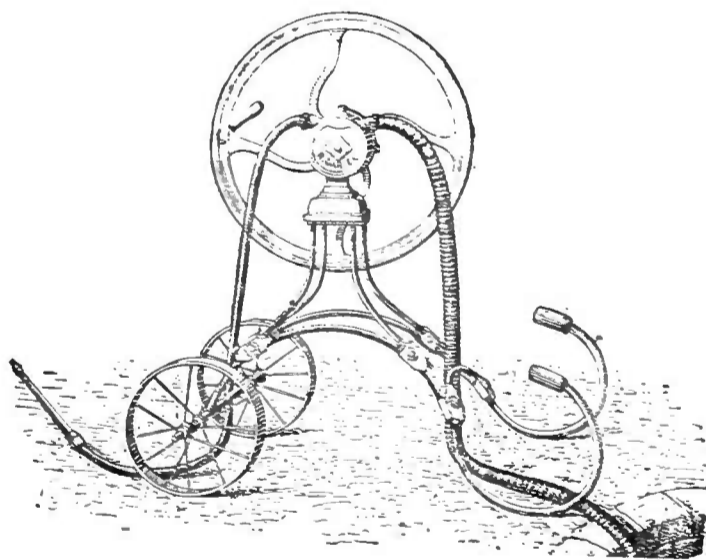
Pompe aspirante et foulante rotative, montée sur brouette.
